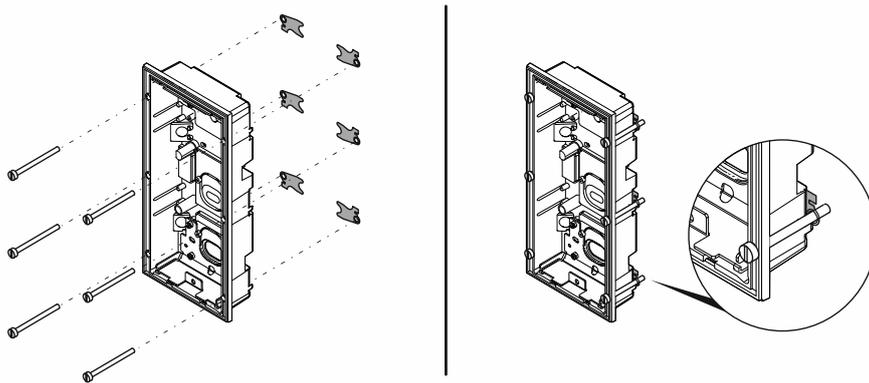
Montageset für Hohlwand Dosen (83511-500)
